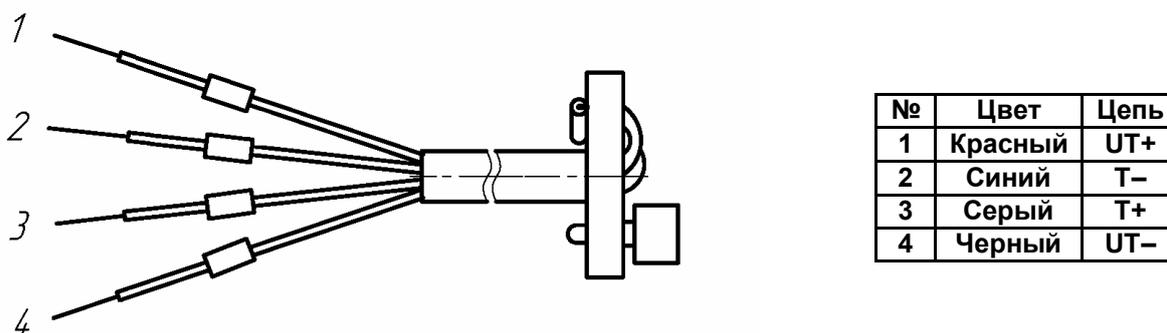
Соединитель И4 (006.304.000)
